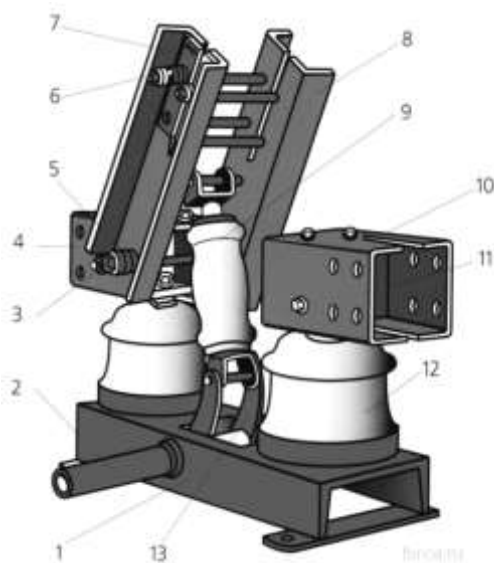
Поліус роз'єднувача РВК-10: 1 - основа; 2 - вал; 3 - вісь, 4 і 10 - нерухомі контакти; 5 і 6 - пружини піджимання; 7 - сталева пластина; 8 - рухомий контакт; 9 - порцеляновий тяга роз'єднувача; 11 - чавунний контакто-утримувач; 12 – опорний ізолятор, 13 - важіль.
